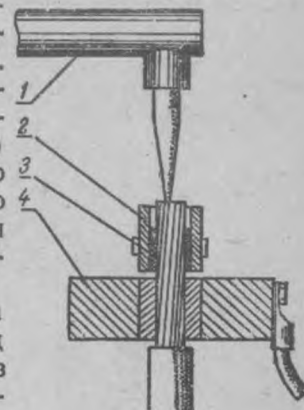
Сварка многопроволочной жилы в монолитный стержень
